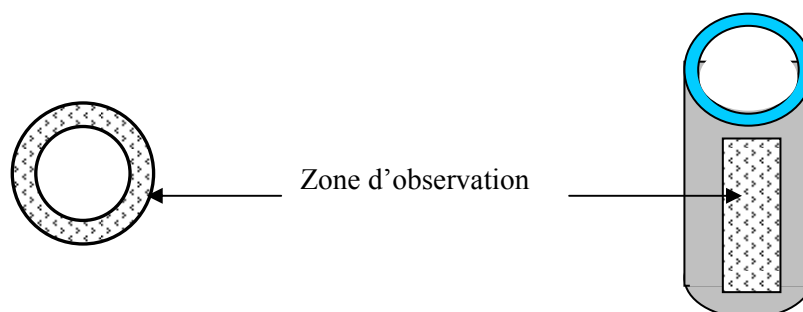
a) coupe transversale - b) coupe longitudinale
